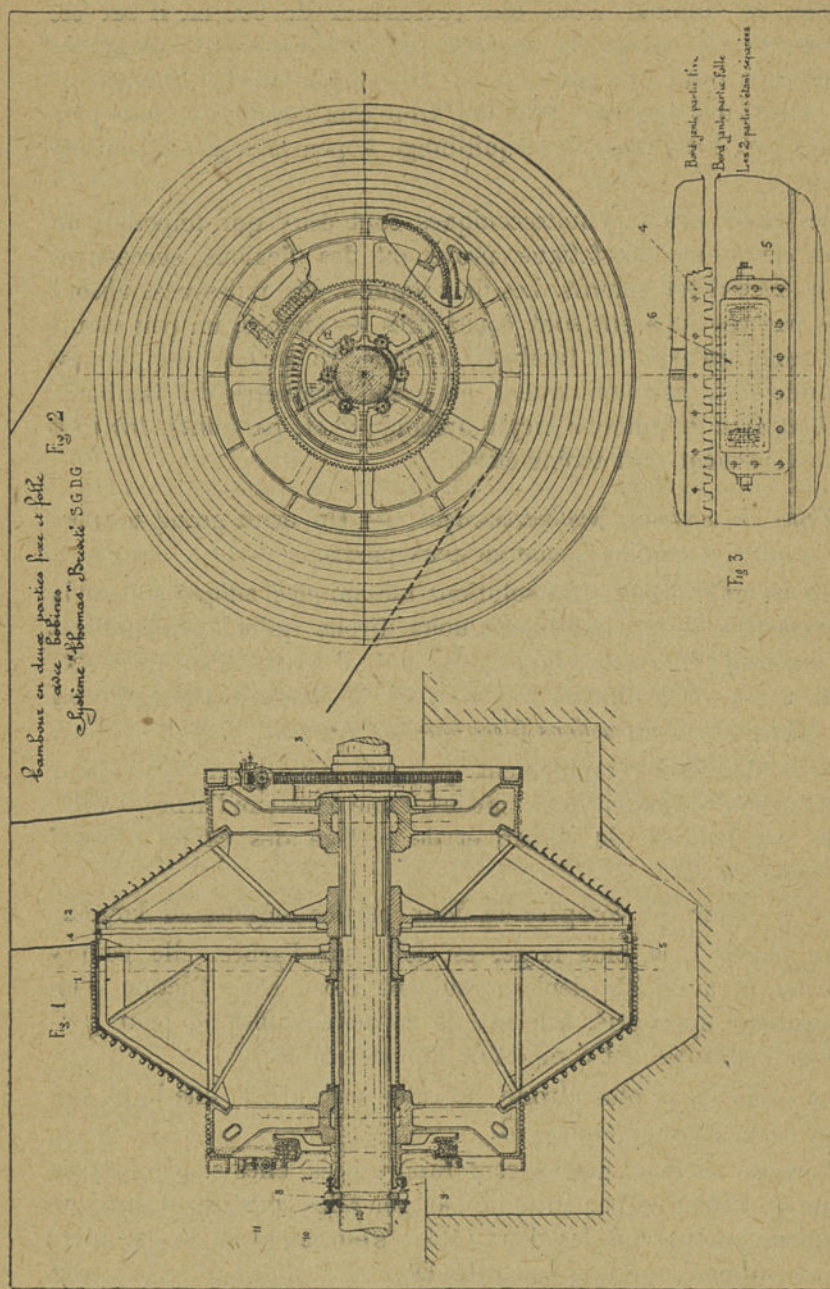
Tambour bicylindro-conique pour machine d'extraction.
